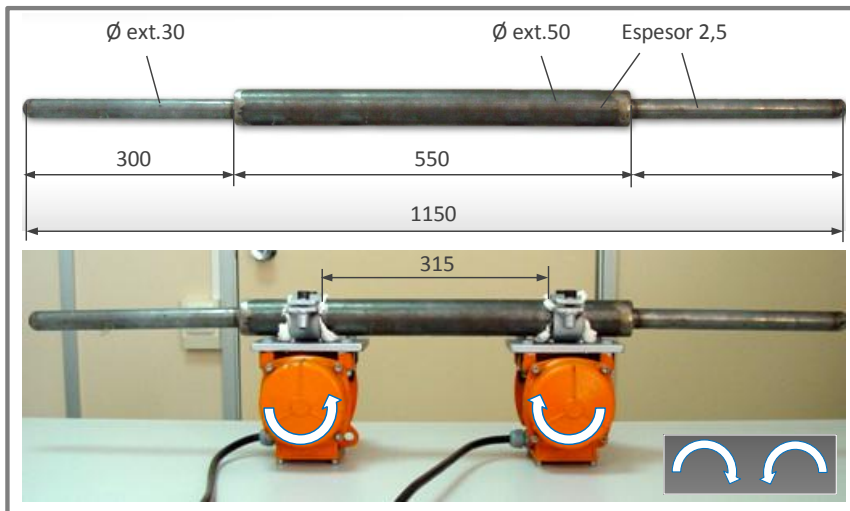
Superior, detalle y dimensiones de la barra fabricada a medida para el desarrollo del prototipo I, formada por tramos de tubo redondo de acero; inferior, vista en alzado lateral del montaje final del prototipo I de barra vibratoria. Las flechas indican las dos opciones posibles de sentido del giro de ambos motores para provocar la contrarrotación deseada.
